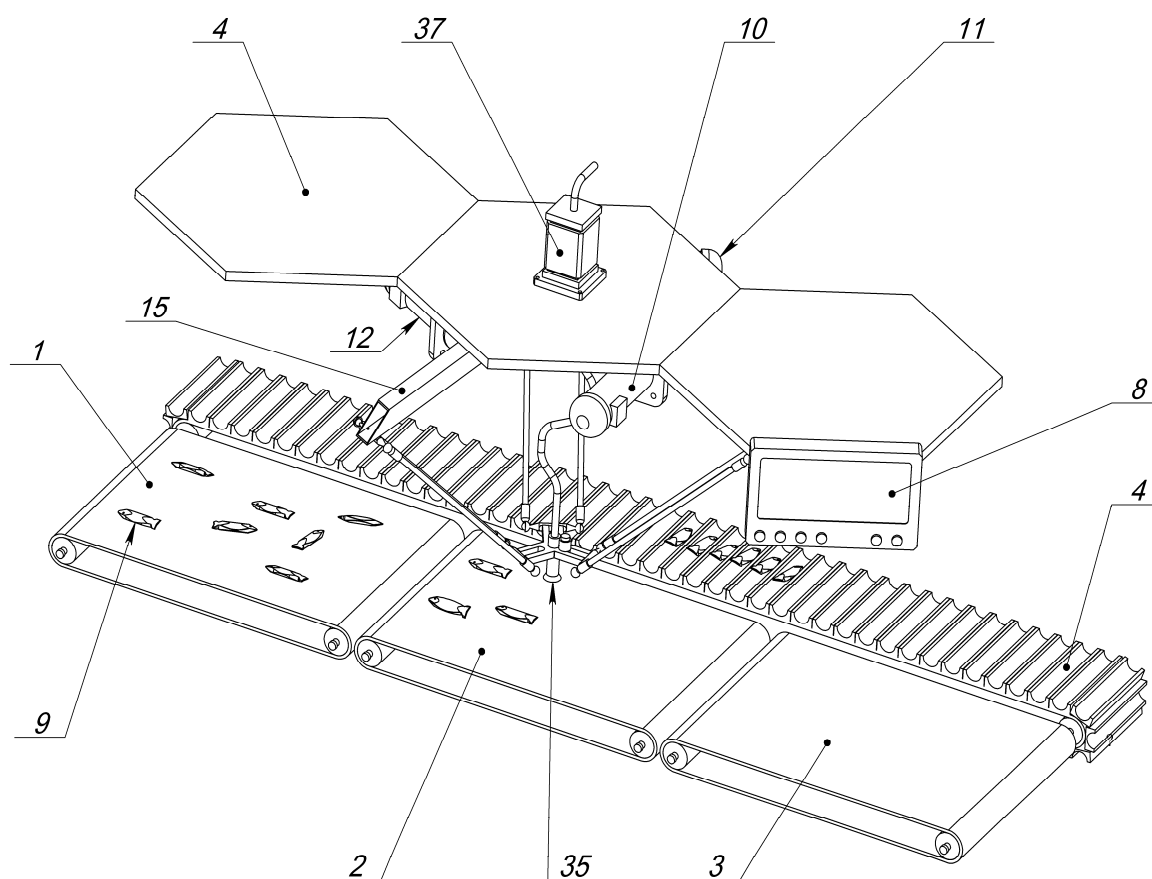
Устройство для загрузки рыбы в рыбообрабатывающие машины, общий вид
